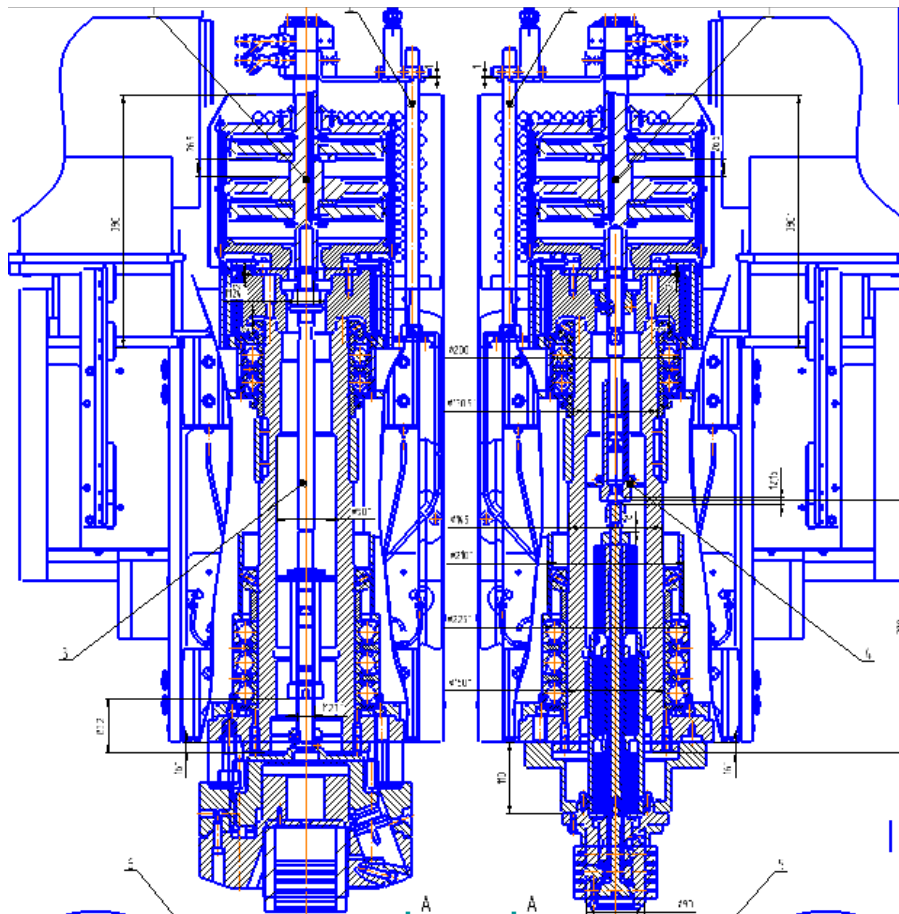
Конструктивна схема шпиндельного вузла верстата
